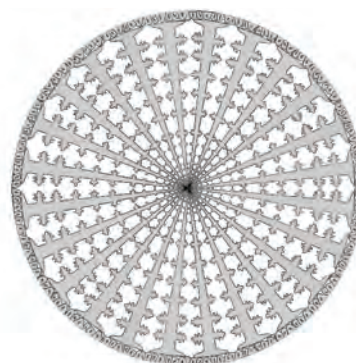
Схема теплофизической модели затвердевания цилиндрической и шаровой отливок при сужении фронта затвердевания в осевой зоне
